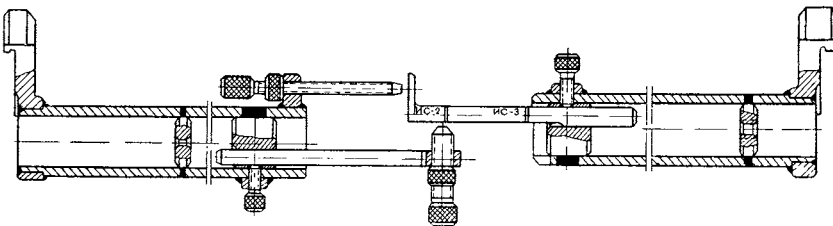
Приспособление 47001-1-003М-1 для центровки бортовых передач
